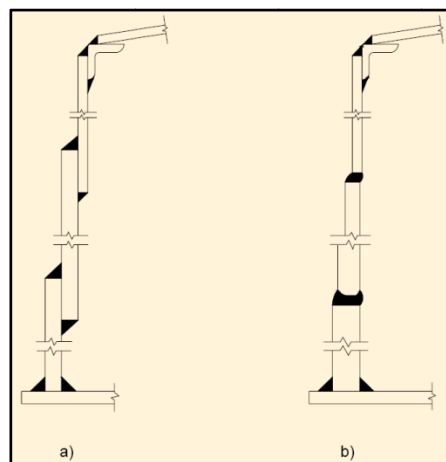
Esquemas de los tipos de unión para las placas de los anillos de cuerpo en un tanque de almacenamiento cilíndrico-vertical, a) Soldadura a traslape, b) Soldadura a tope
